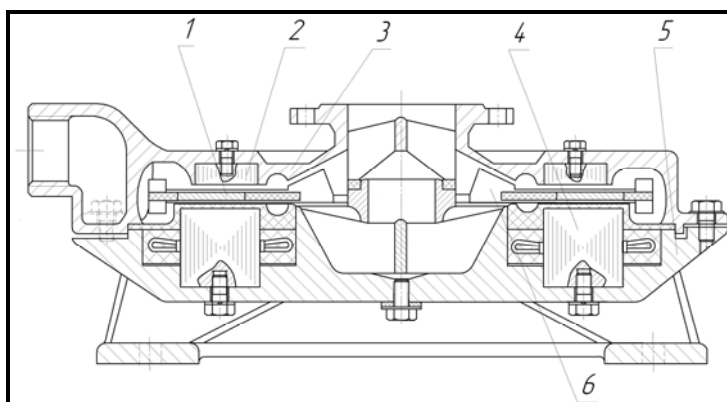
Насос с бесконтактным приводом рабочего колеса: 1 – рабочее колесо; 2 – верхний элемент индуктора; 3 – крышка; 4 – статор асинхронного торцевого двигателя; 5 – корпус; 6 – лопатки.
